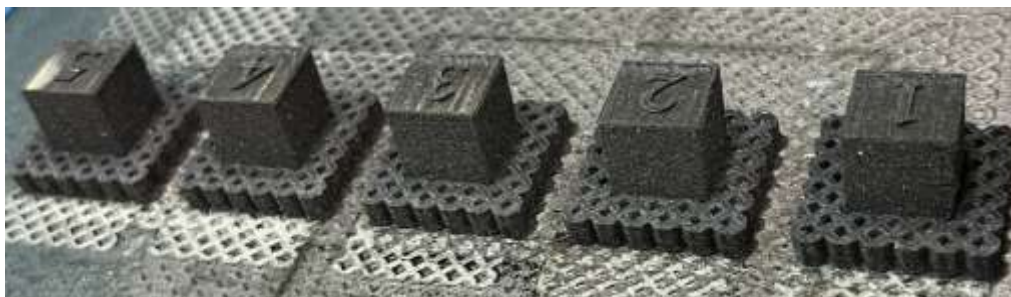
Исходные пористые СЛС-заготовки образцов
